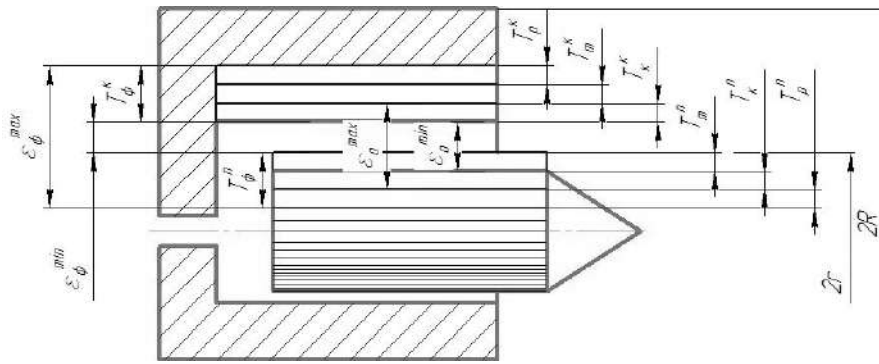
Схема расположения допусков поршневой пары аксиально-поршневой гидромашины
